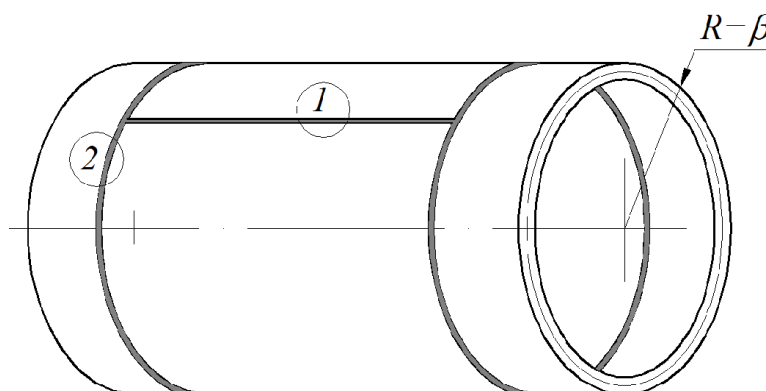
Сварная конструкция подпиточного бака
